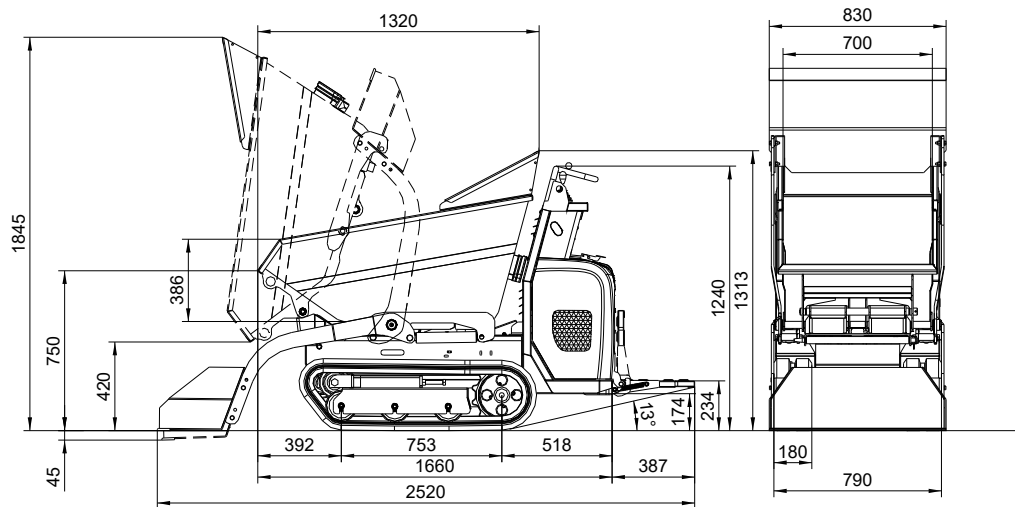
Dimensions de la machine (modèle DT08-D avec benne)
